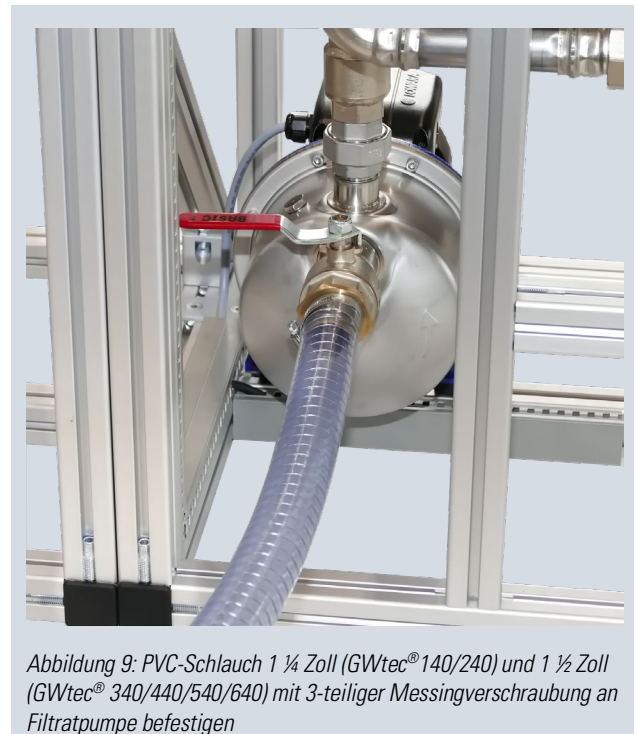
PVC-Schlauch 1 ¼ Zoll (GWtec® 140/240) und 1 ½ Zoll (GWtec® 340/440/540/640) mit 3-teiliger Messingverschraubung an Filtratpumpe befestigen
